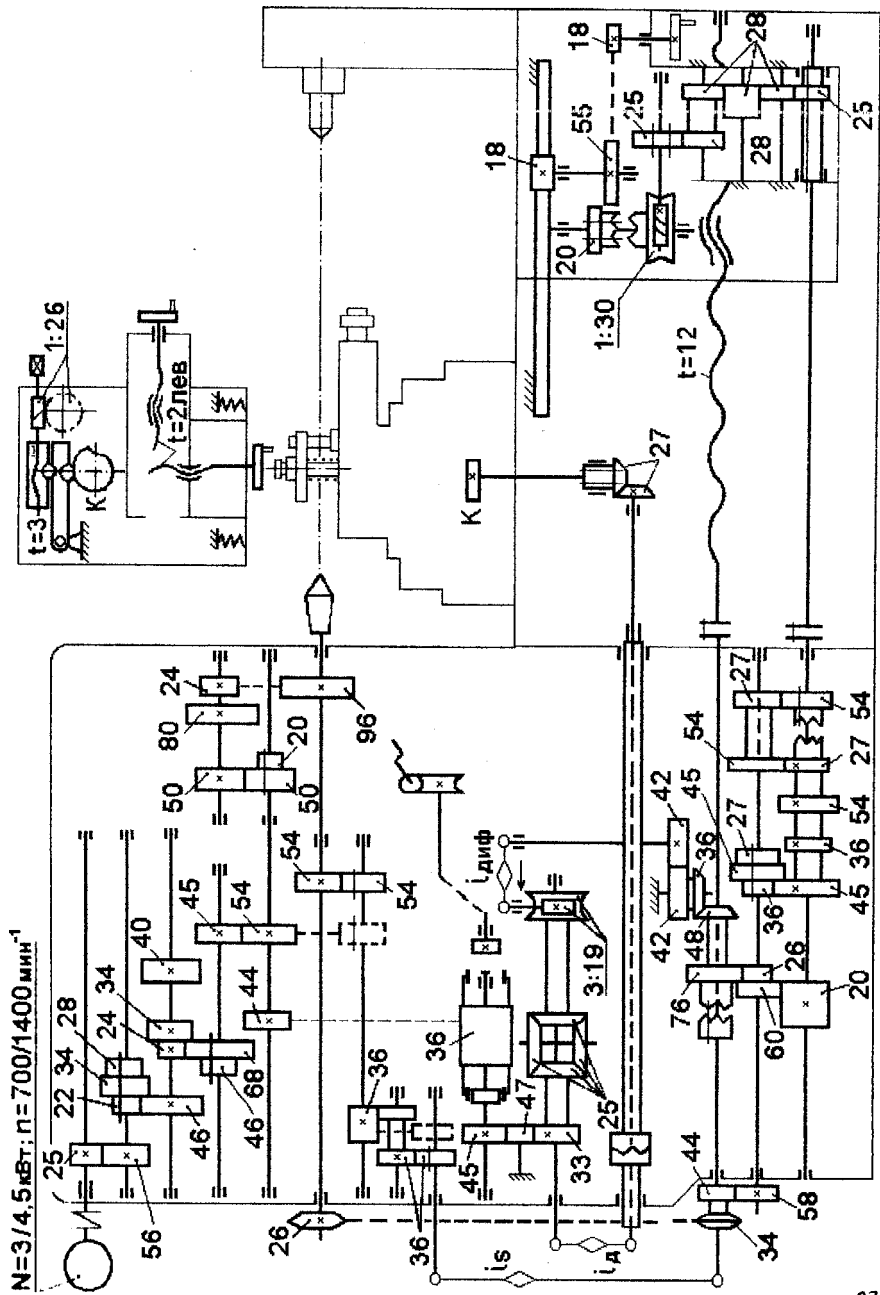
Кинематическая схема токарно-затыловочного станка модели 1Б81
